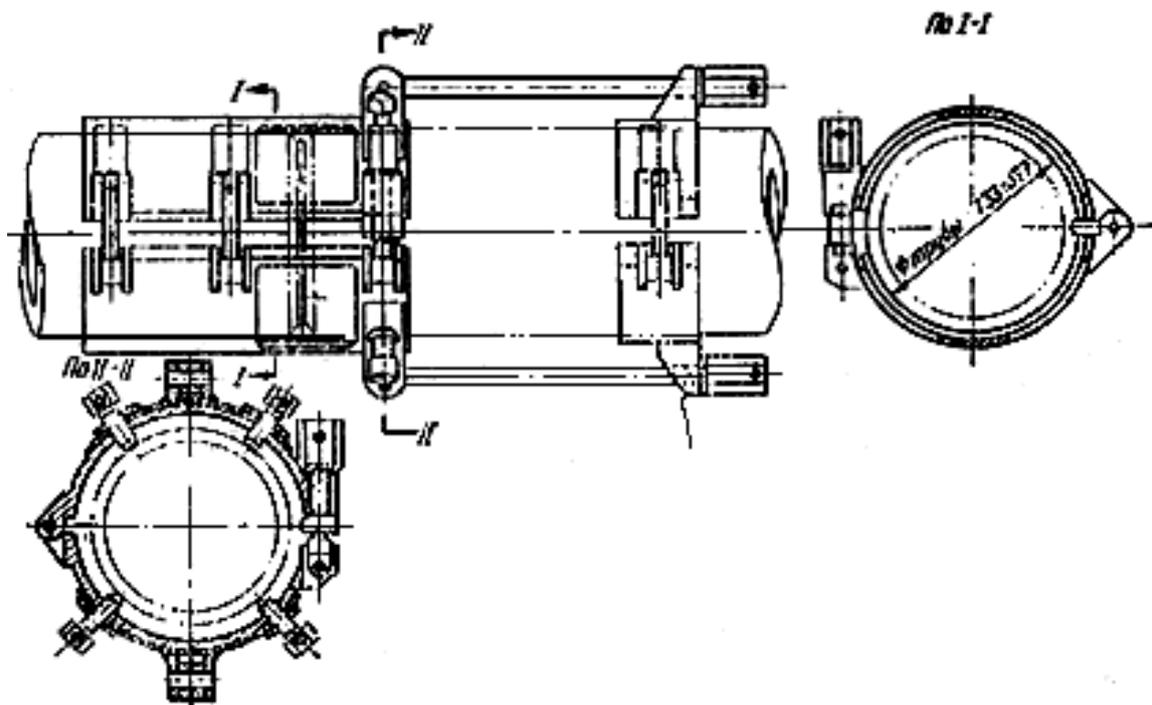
Приспособление хомутового типа для центровки труб из низколегированных сталей диаметром 133...377 мм
